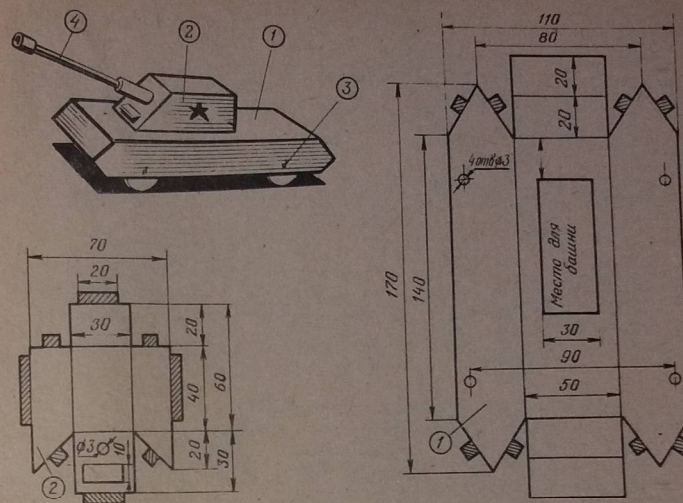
Модель танка: 1 — корпус; 2 — башня; 3 — ось; 4 — ствол
